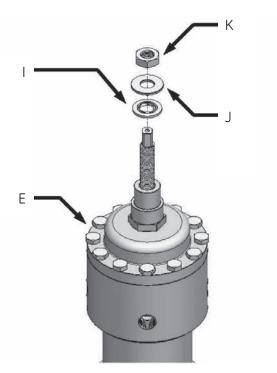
Assemblaggio tenuta filettatura 1000/1500-CH
